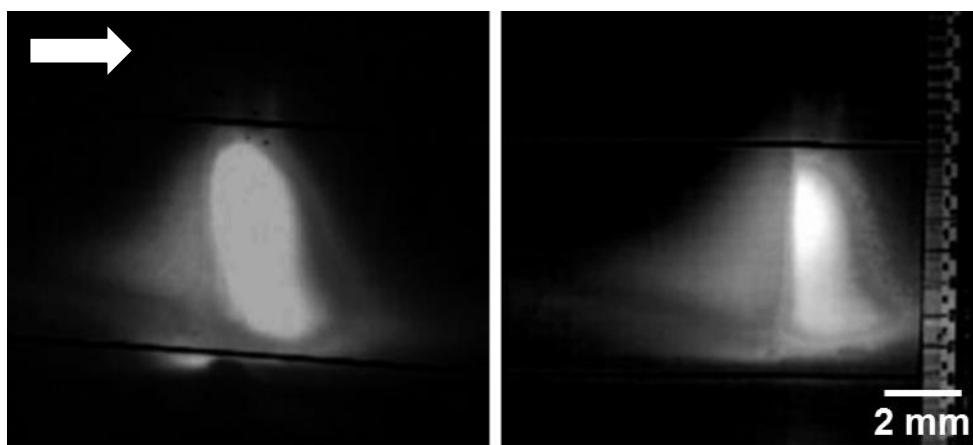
Imagens do arco elétrico da soldagem A-MIG com  $\text{SiO}_2$  a 190A. A direção de soldagem é indicada pela seta.
